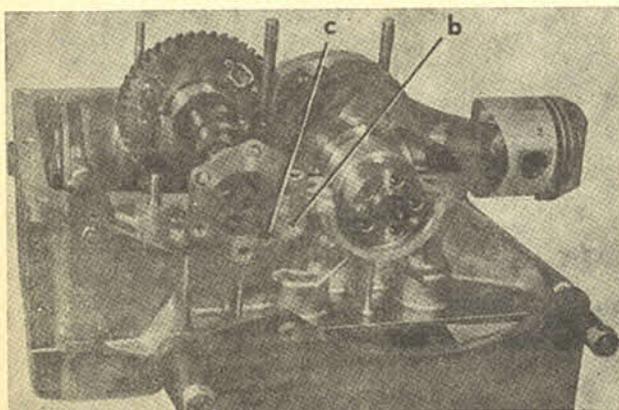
Die Durchtrittsbohrungen «b» und «c» müssen sich bei der Montage decken!
